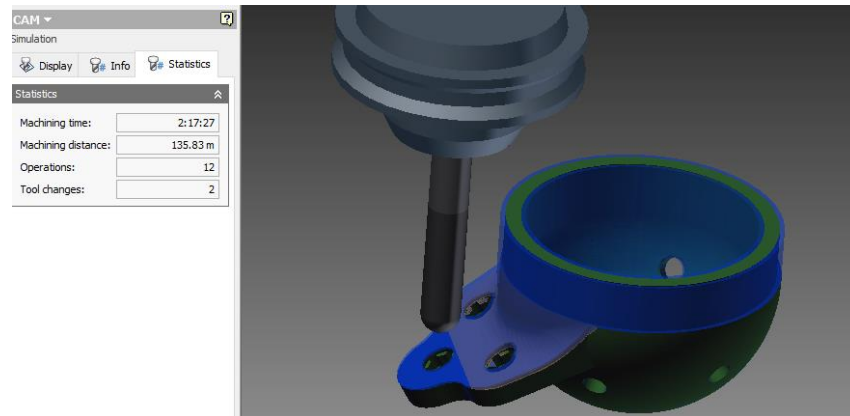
На даному етапі отримуємо машинний час 2:17:27, готову базу і внутрішню поверхню сфери після тонкого фрезерування
